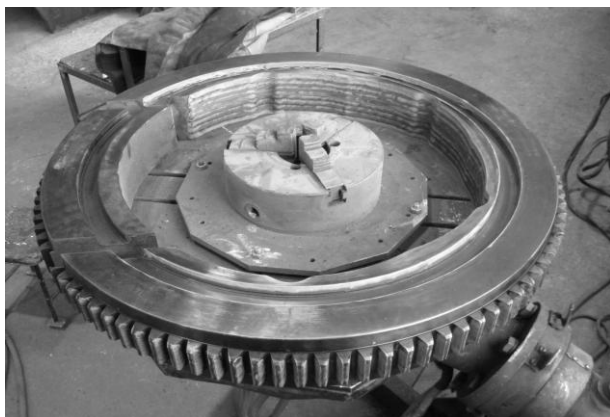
Шестерня поворотная патрона бурового станка с плазменной закалкой
